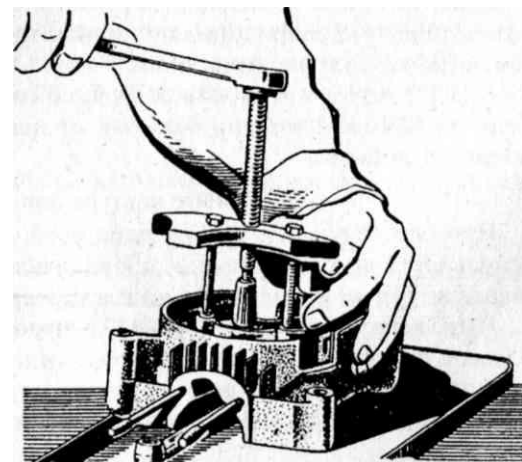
Выпрессовка коленчатого вала при помощи специального приспособления
